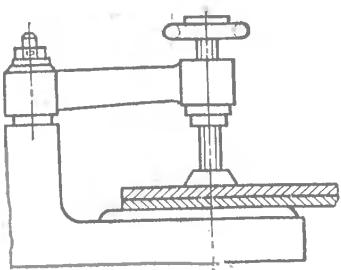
Пристобления для проверки точности сборки под сварку:
